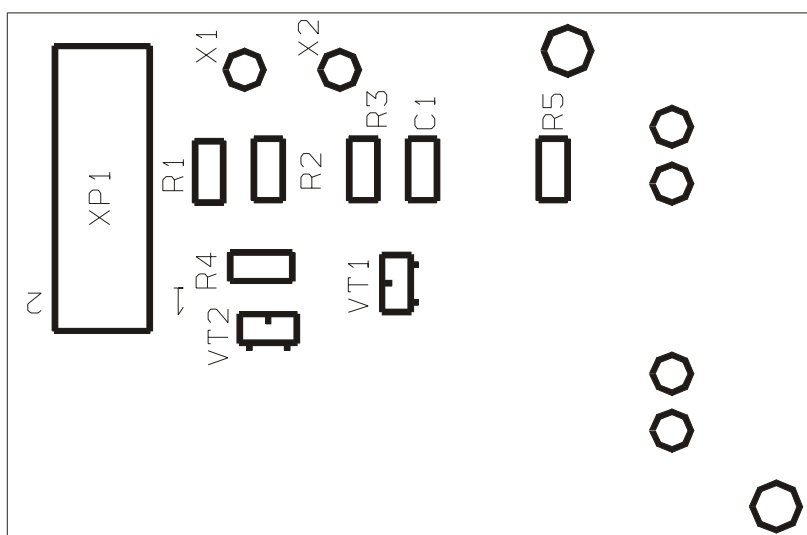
Сборочный чертеж платы блока газоподачи на м/с. TDA1151. Сторона монтажа.
